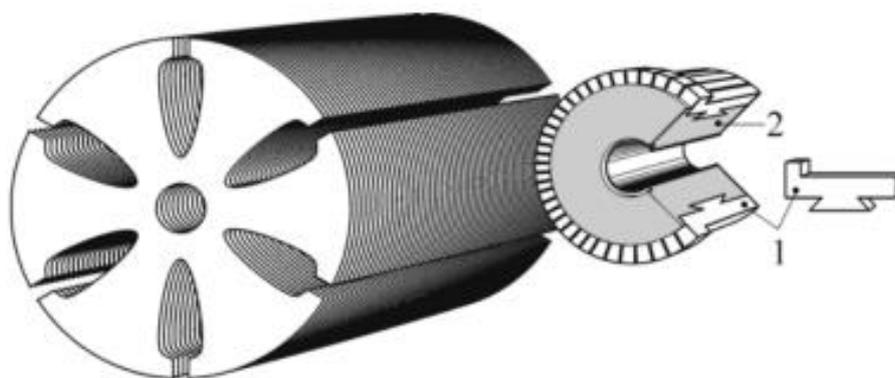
Конструкции магнитопровода и коллектора якоря: 1 – пластина медная; 2 – втулка пластмассовая
